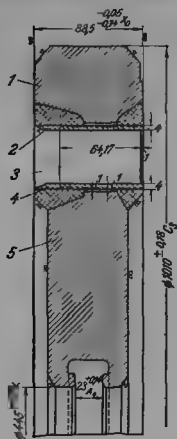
Сварная диафрагма ХТГЗ.
